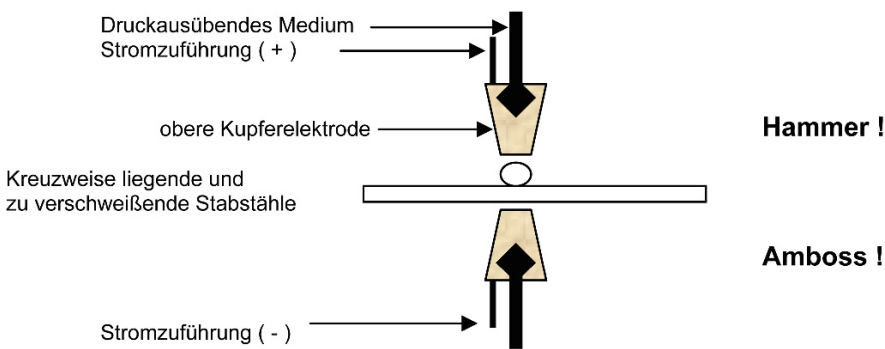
Das Prinzip des Widerstandpunktschweißens
